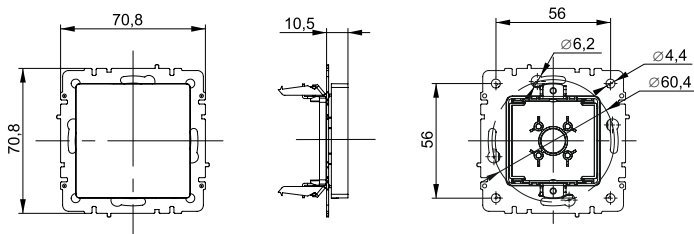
Габаритные и установочные размеры заглушки / Figure 2 – Overall and installation dimensions of the plug /
